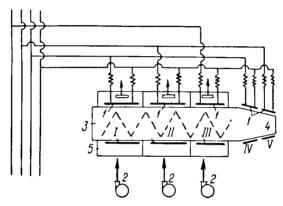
Схема электронагревания и воздушного охлаждения по зонам цилиндра I-V: I—электронагреватели; 2—воздушный вентилятор; 3— цилиндр червячного пресса; 4—головка; 5—кожух цилиндра.
